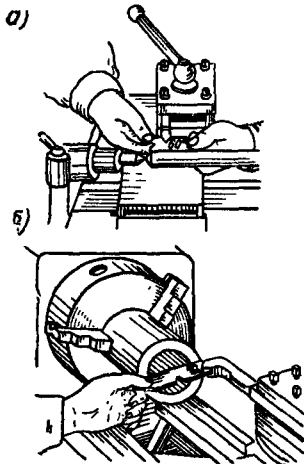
Установка резьбового резца по шаблону для нарезания резьбы: а—наружной; б—внутренней.
